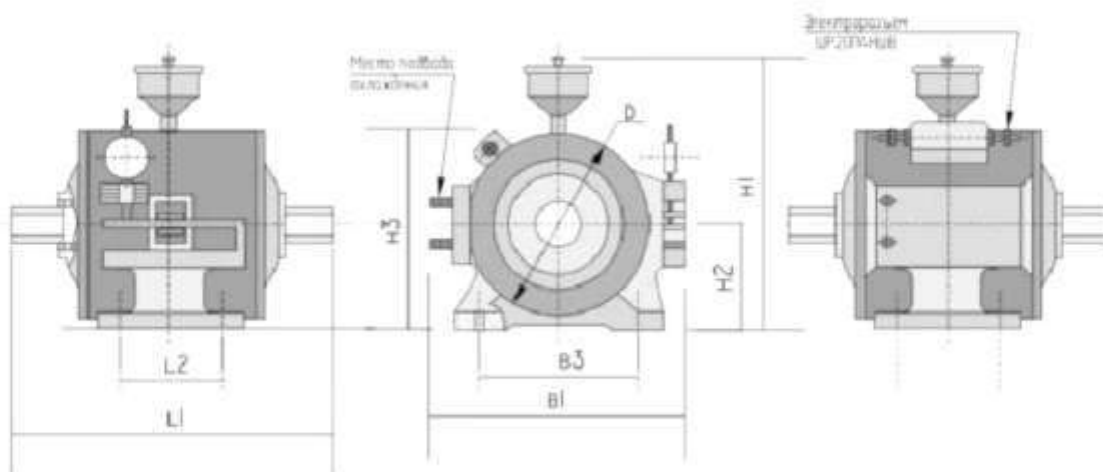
Габаритные и присоединительные размеры тормоза ПТ-6М1
